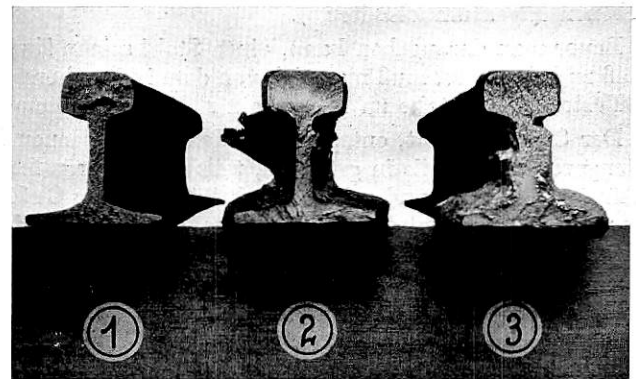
1 = ungeschweißt, 2 = geschweißt und normal geglüht, 3 = geschweißt, ungeglüht.
